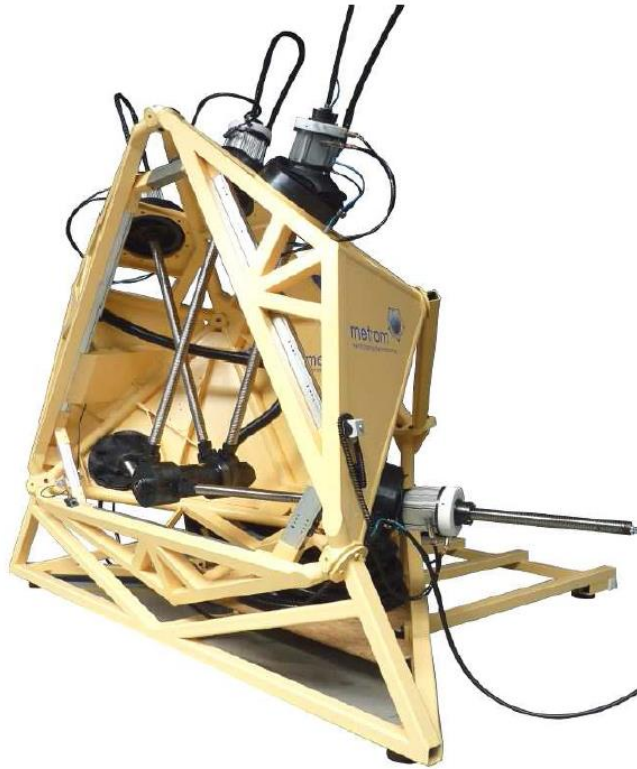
Фрезерний станок з паралельною кінематикою [3]
